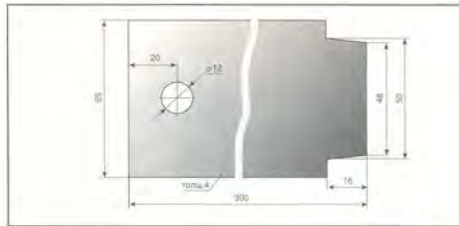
Ключ для регул. гайки правого подшипника дифференциала переднего моста автомобиля ВАЗ-2121.
